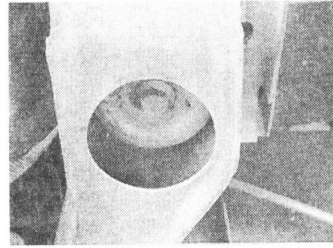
с. Передний болт крепления подрамника к корпусу автомобиля.
